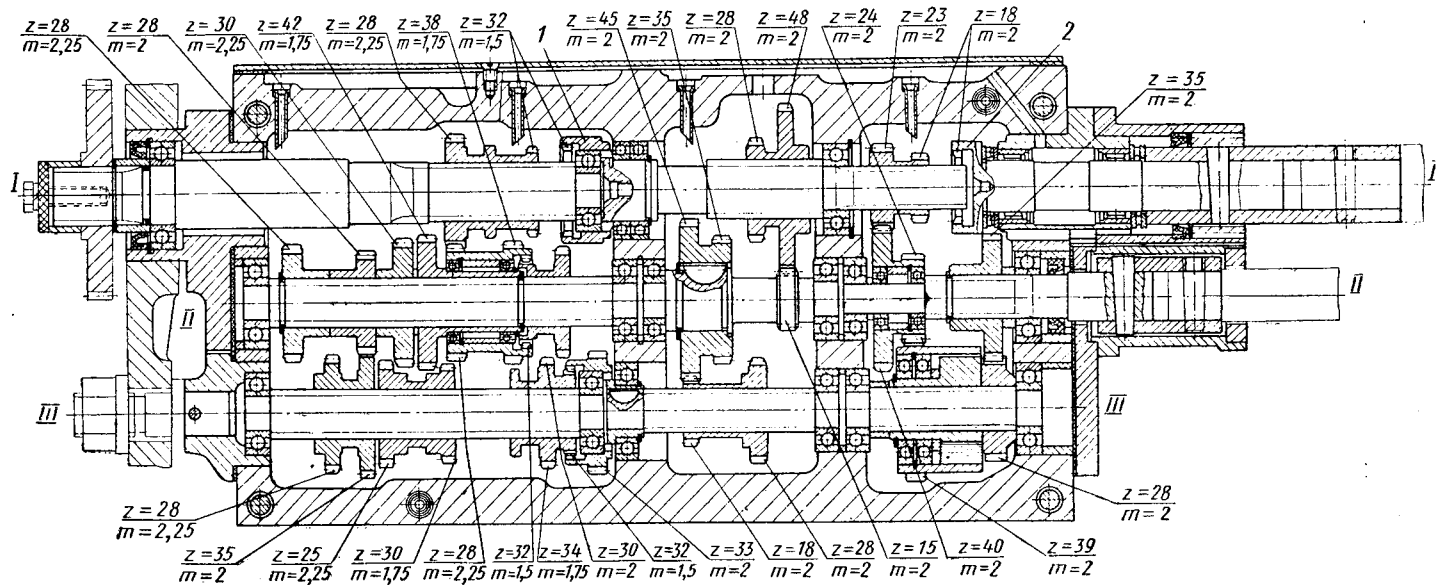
Развертка унифицированной коробки подач станка средней гаммы
